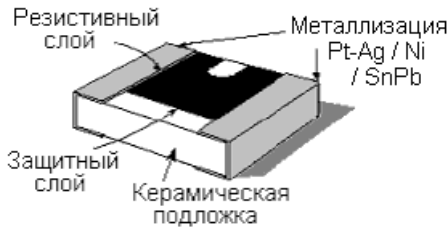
Конструкція чіп-резистора для поверхневого монтажу
